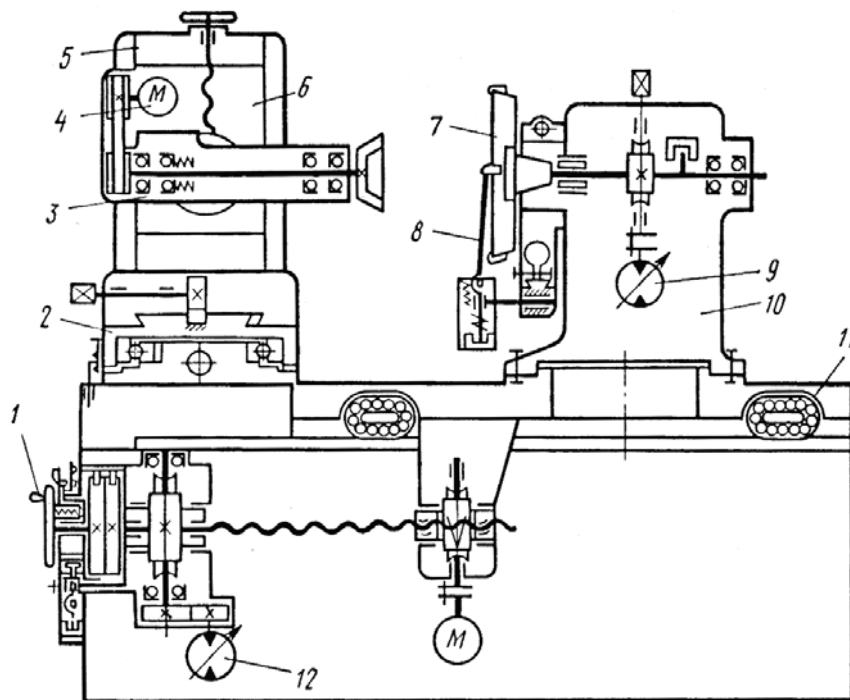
Общий вид заточного станка для сверл мод. ВЗ-322
